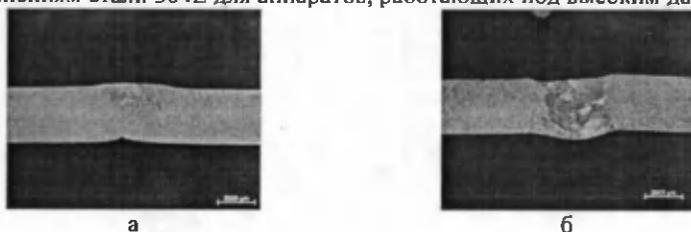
Макрошлифы сварных швов нержавеющей стали 304L (толщина 3 мм), полученные при аргодуговой сварке обычной технологией (а) и с подачей газопорошковой смеси в зону сварки (б)
